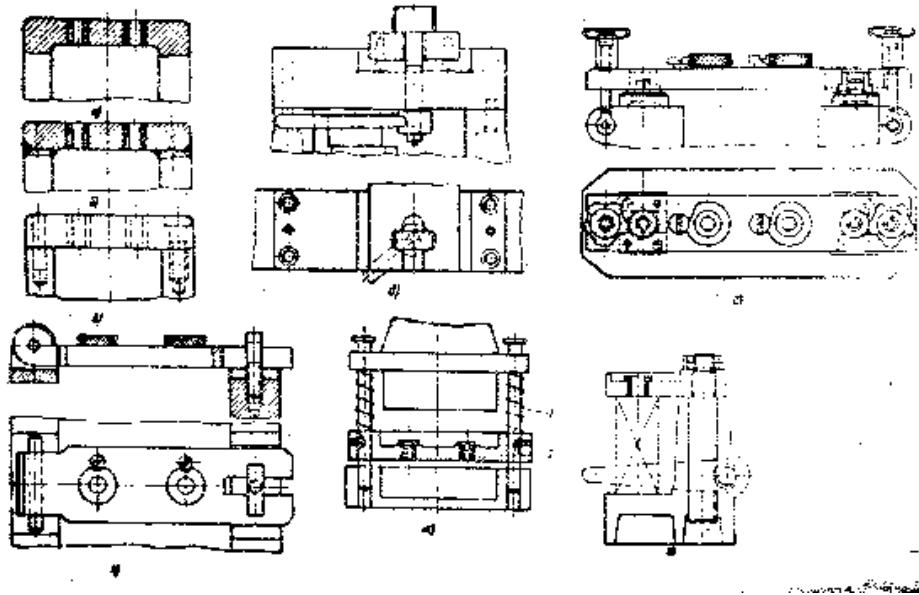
Кондукторные плиты сверлильных приспособлений.
